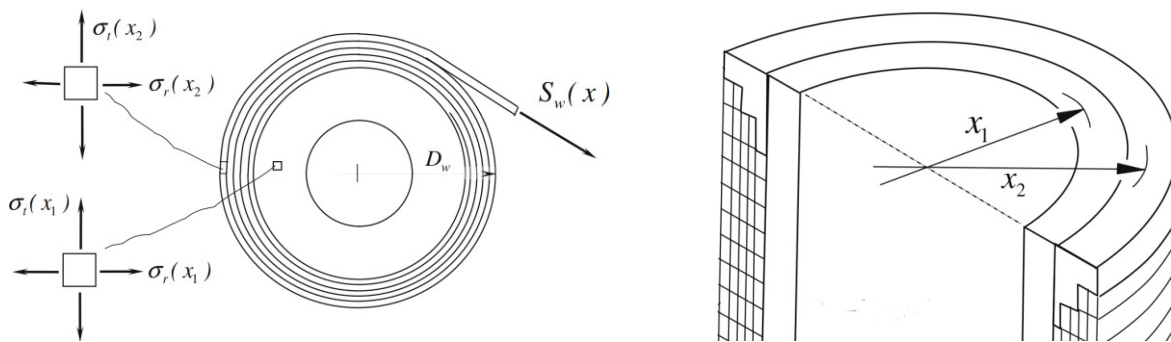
Схема многослойной конструкции для сборки корпуса сосуда давления, намотанная узкой стальной лентой
